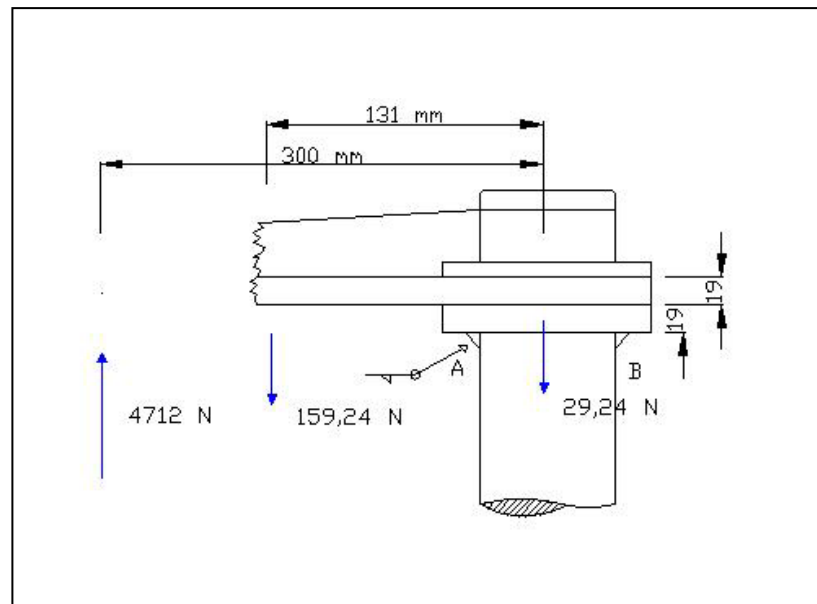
43. Soldadura de la brida superior. Fuente: Los Autores.
